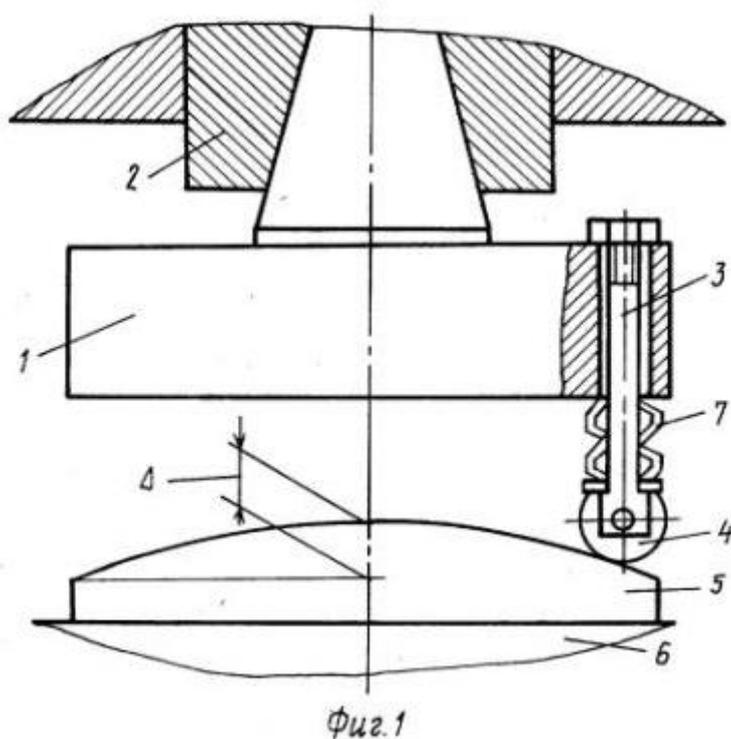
Устройство для нагружения фрезерных станков.
